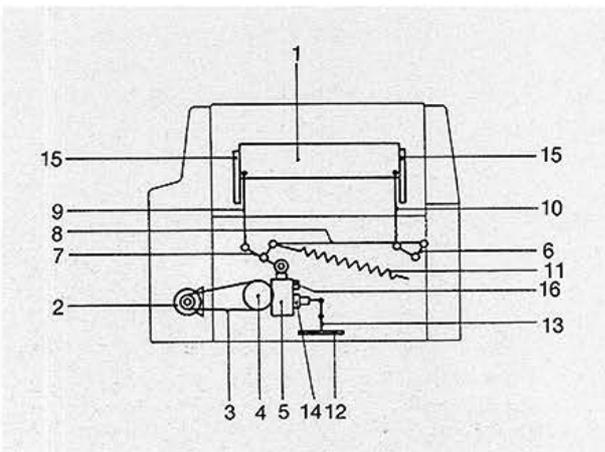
Hydraulische Pressung an einer Schneidemaschine: 1 Preßbalken, 2 Motor, 3 Riemen, 4 Hydraulikpumpe, 5 Hydraulikaggregat, 6, 7 Hebel, 8, 9, 10 Zugstangen, 11 Rückhol- und Ausgleichsfeder, 12, 13 Schnittandeuterpedal mit Gestänge, 14 Steuermagnet, 15 Führungsleisten
